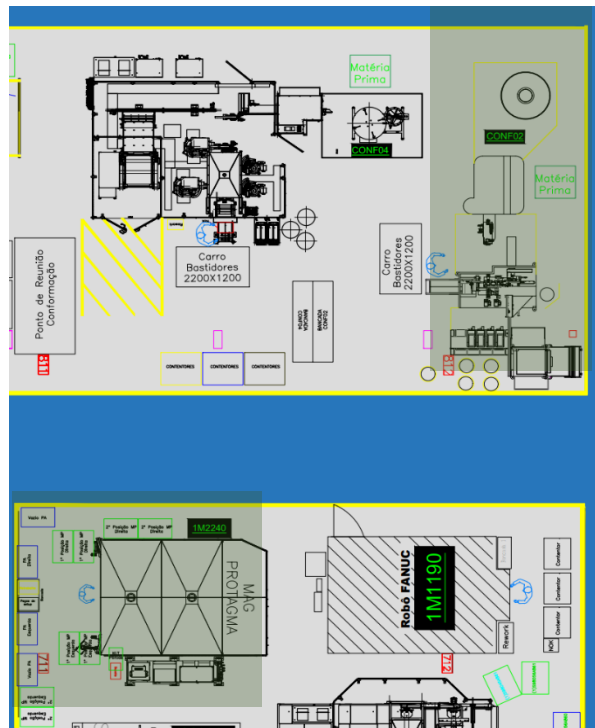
Layout* detalhado da CONF02 e da 1M2240.
